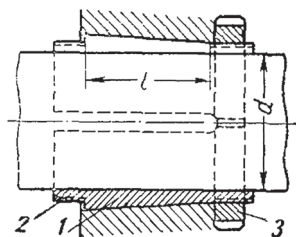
Закрепление детали на гладком валу без шпонки
